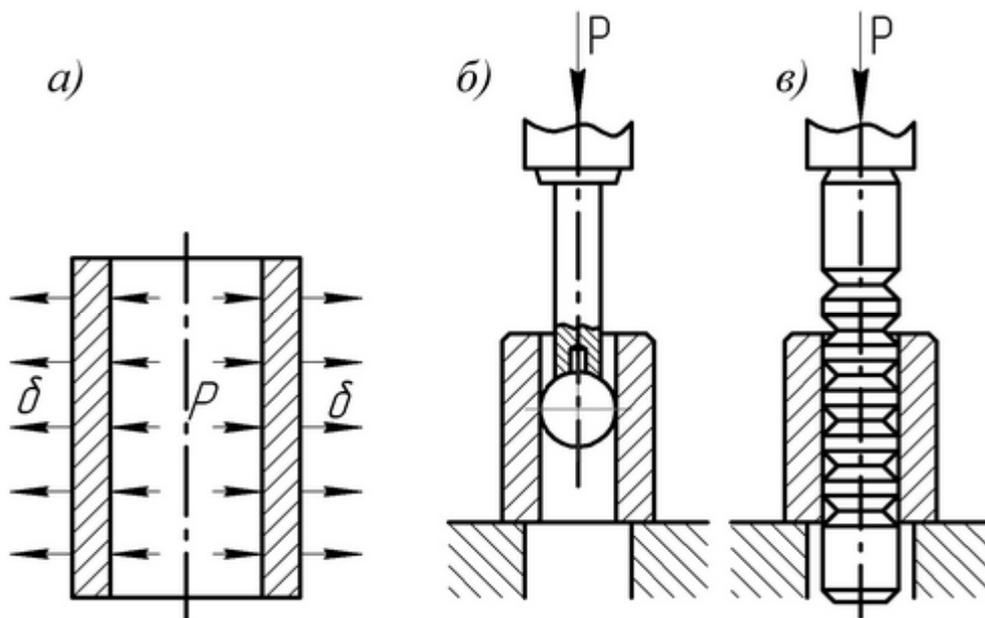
Раздача: а – схема обработки; б – раздача шариком; в – раздача цилиндрической оправкой
